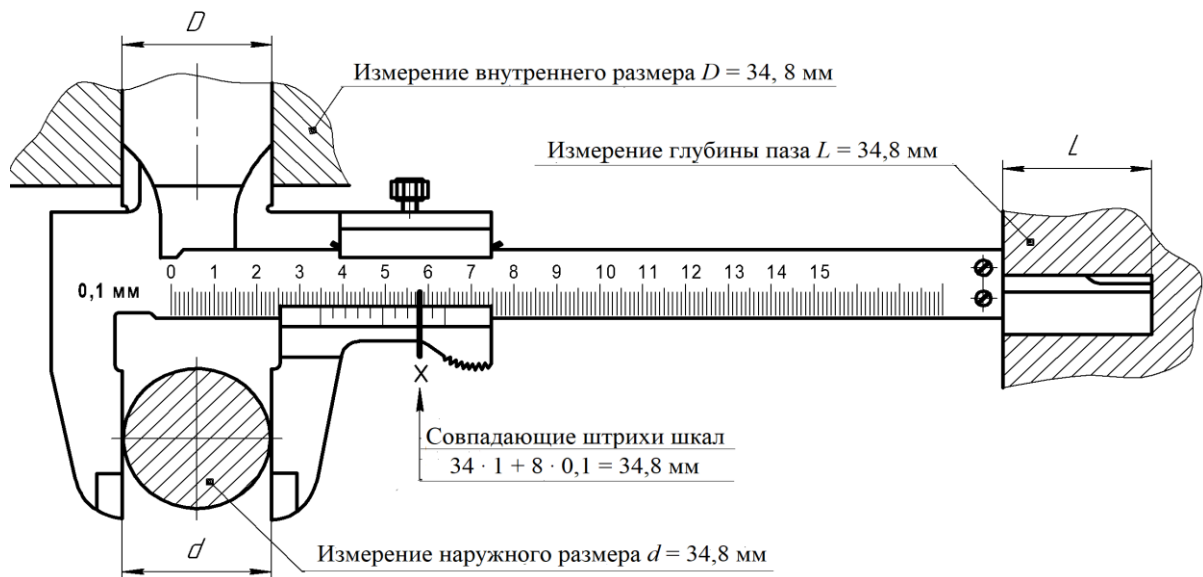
Измерение размеров деталей штангенциркулем типа I
